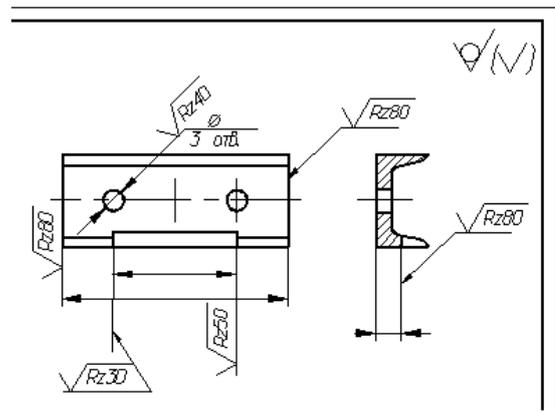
Указание шероховатости, когда большая часть поверхностей не обрабатывается по данному чертежу
